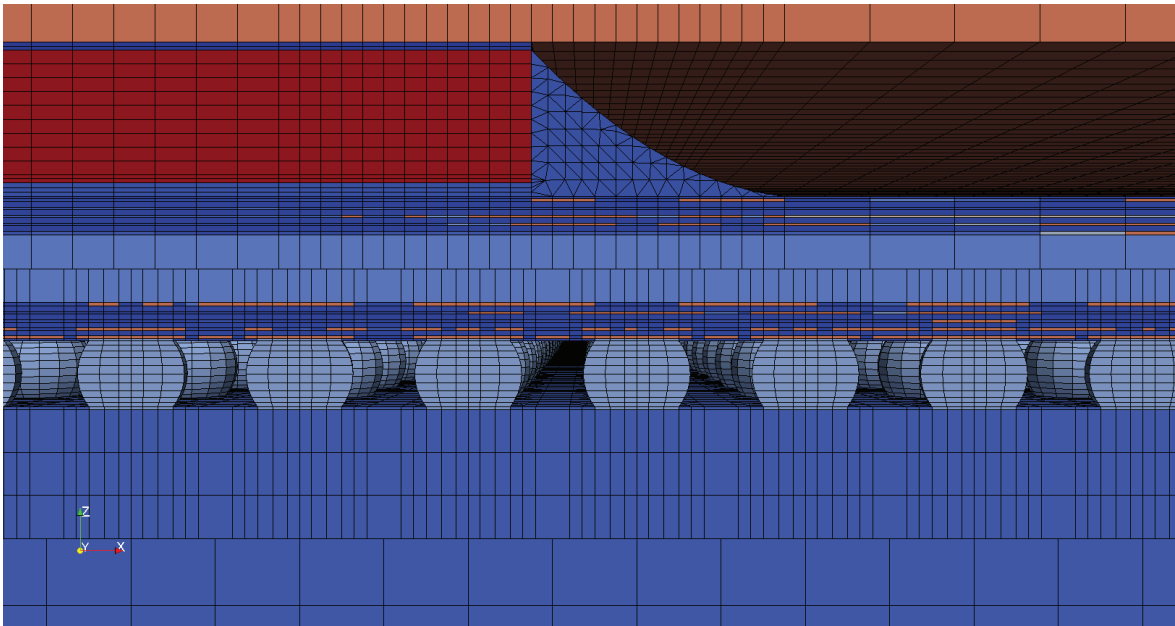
Vue de coupe d'un maillage d'assemblage à la carte
